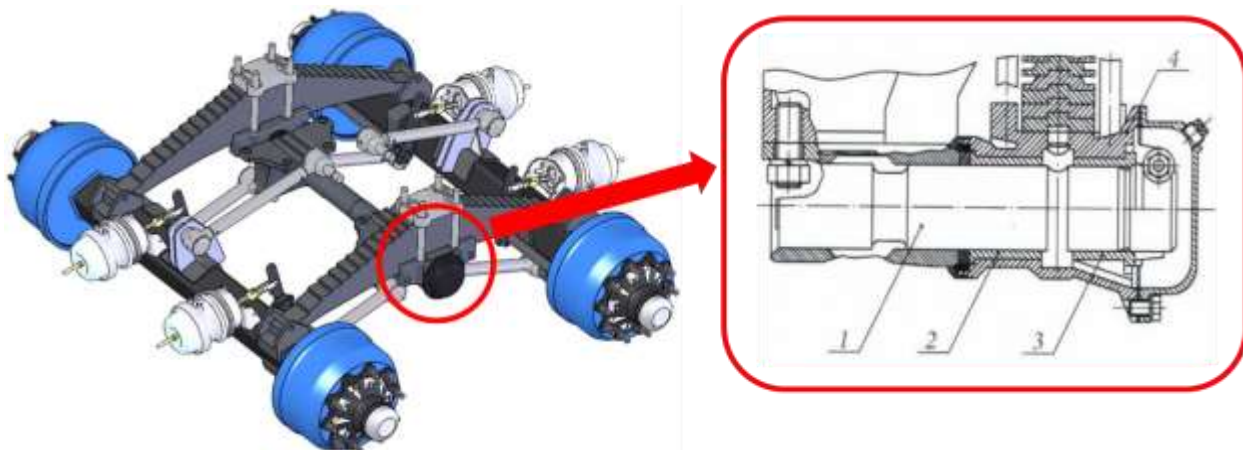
Балансирная подвески автомобиля и схема установки подшипников скольжения
